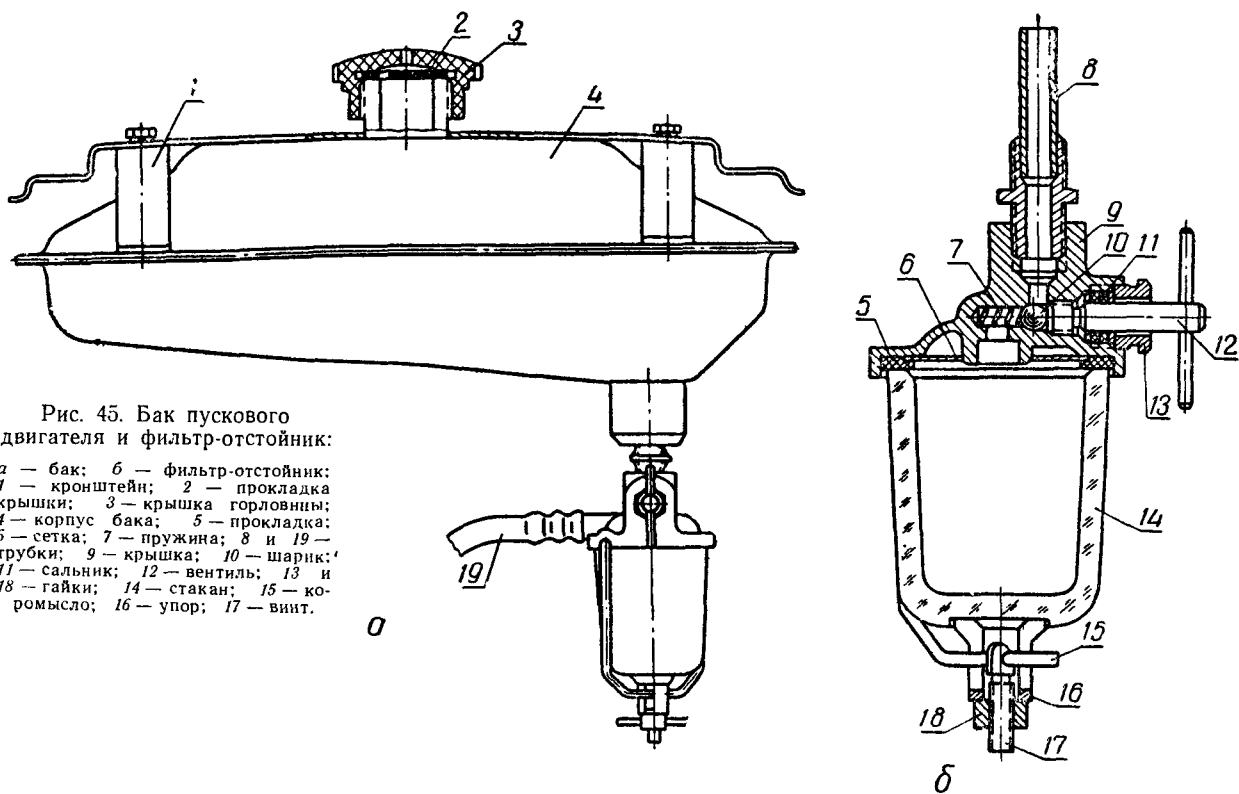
Бак пускового двигателя и фильтр-отстойник:
